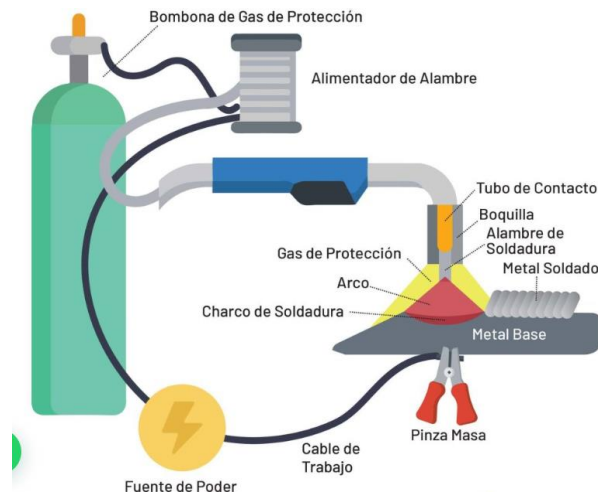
Esquema de un equipo de soldadura MIG. Fuente:
